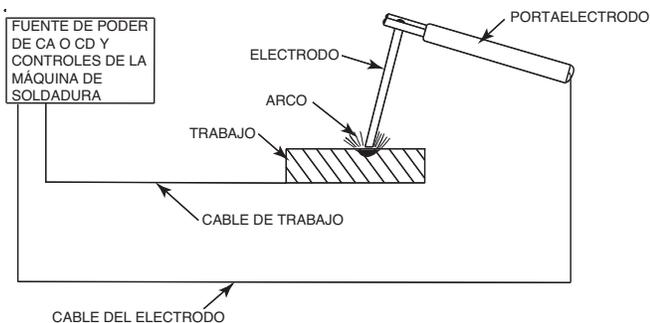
El circuito de soldadura para soldadura de arco metálico protegida (Electrodo Revestido).
